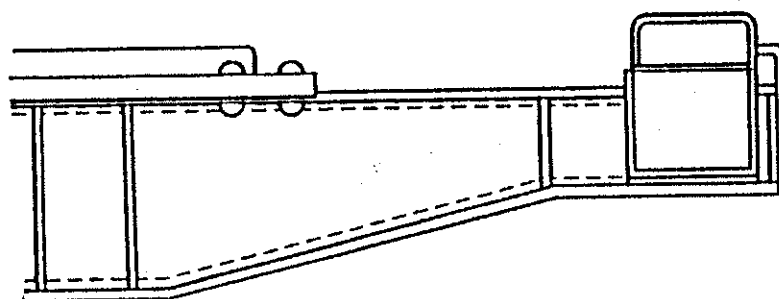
Контроль сварных соединений боковой стенки с верхней и нижней пластинами
